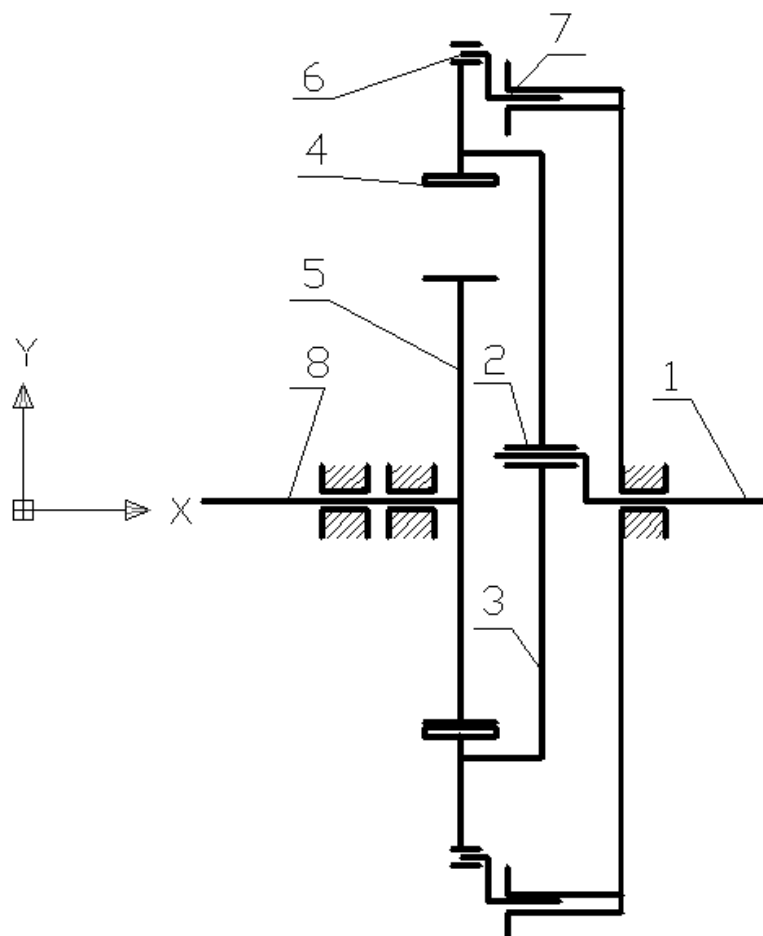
Эксцентриковая передача с поступательным движением сателлита: 1 – входной вал; 2 – эксцентриковый кривошип; 3 – сателлит; 4 – внутреннее зубчатое колесо; 5 – центральное колесо; 6 – эксцентрик; 7 – дополнительный вал; 8 – выходной вал
